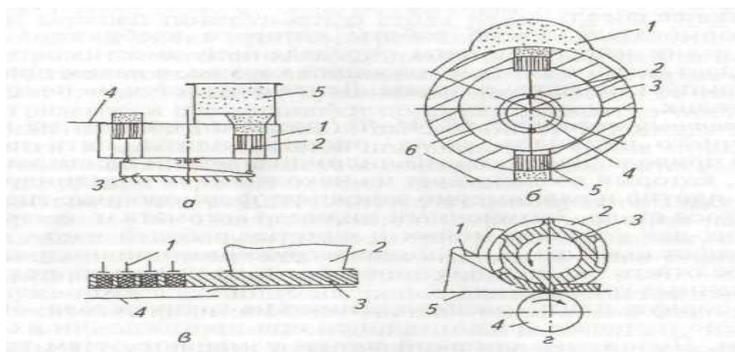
Схема работы устройств для формирования котлет: а - однорядного типа: 1 - стол; 2 - поршень; 3 - копир; 4 - диск; 5 - питатель; б - многорядного типа: 1 - питатель с избыточным давлением фарша; 2 - ролик; 3 - барабан; 4 - кулачок; 5 - поршень; 6 - лоток; в - с многогнездовой плитой: 1 - поршень; 2 - питатель; 3 - плита; 4 - лоток; г - с карманами: 1 - питатель; 2 - карман; 3 - валик; 4 - поддерживающий валик; 5 - лента.
